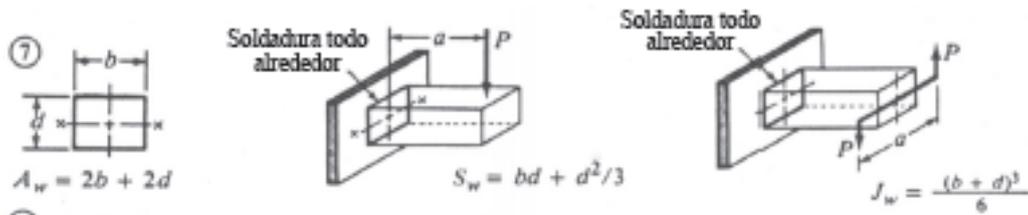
Factores Geométricos para Analizar Soldadura como Línea
